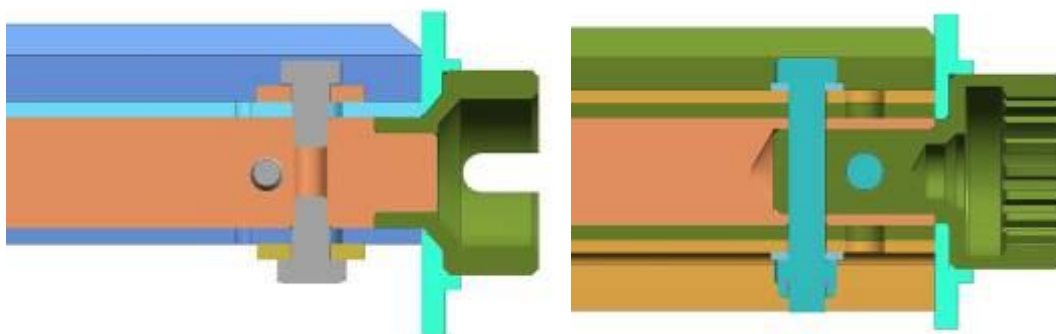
Соединение вальца и приводной полумуфты серийного приспособления (слева) и жатки RSM MS-870-49 (справа)
